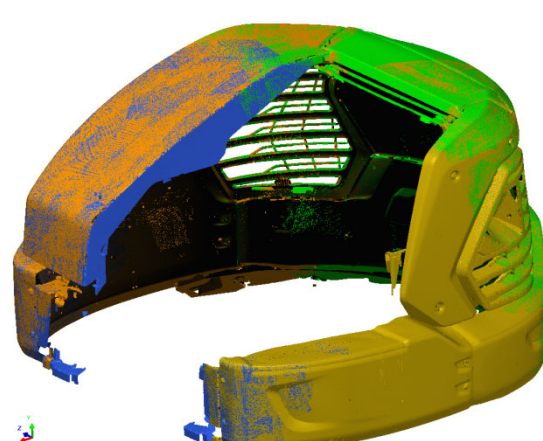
Ruční před-vyrovnání dvou mraček bodů
